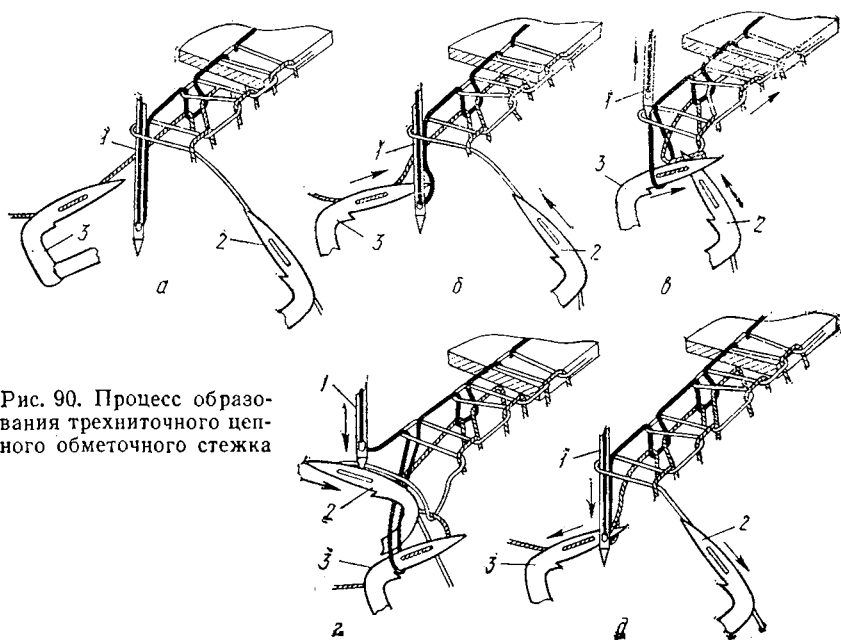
Процесс образования трехниточного цепного обметочного стежка
